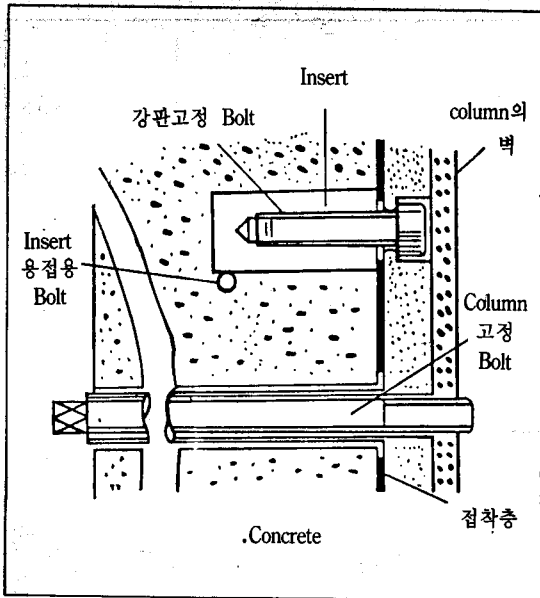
Concrete Bed와 column의 결합방법의 예 (MTIRA)
